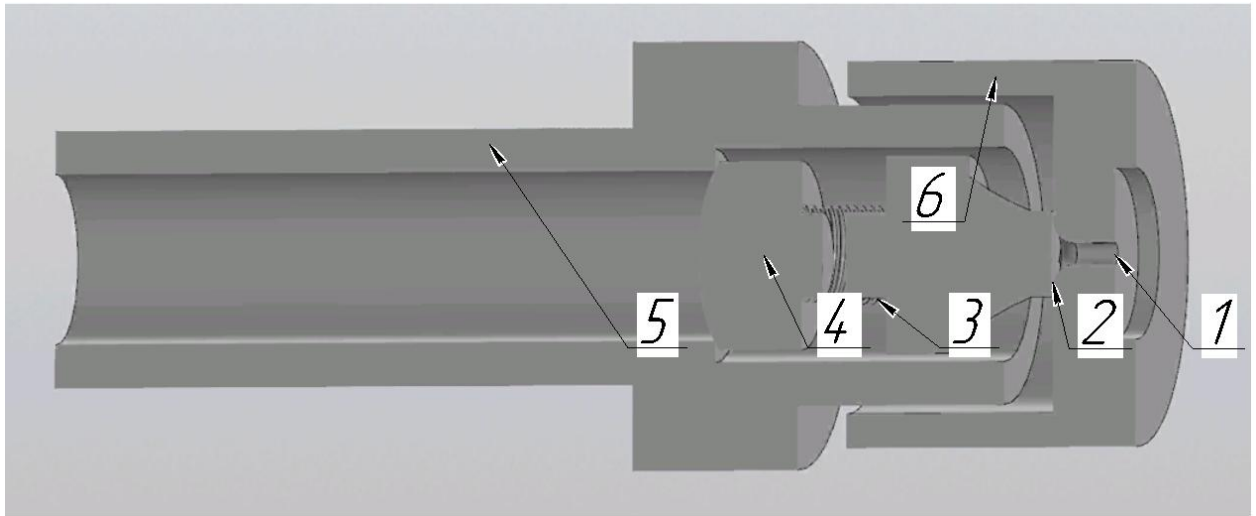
3D модель туманоутворюючої форсунки: 1 – сопловий отвір; 2 – керамічна вставка; 3 – пружина; 4 – резиновий клапан; 5 – корпус форсунки; 6 – корпус розпилювача.
